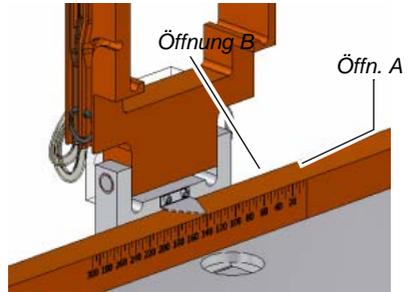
T-Schlüssel in Öffnung A stecken, mit Sechskantschlüssel Bolzen in Öffnung B lösen.
